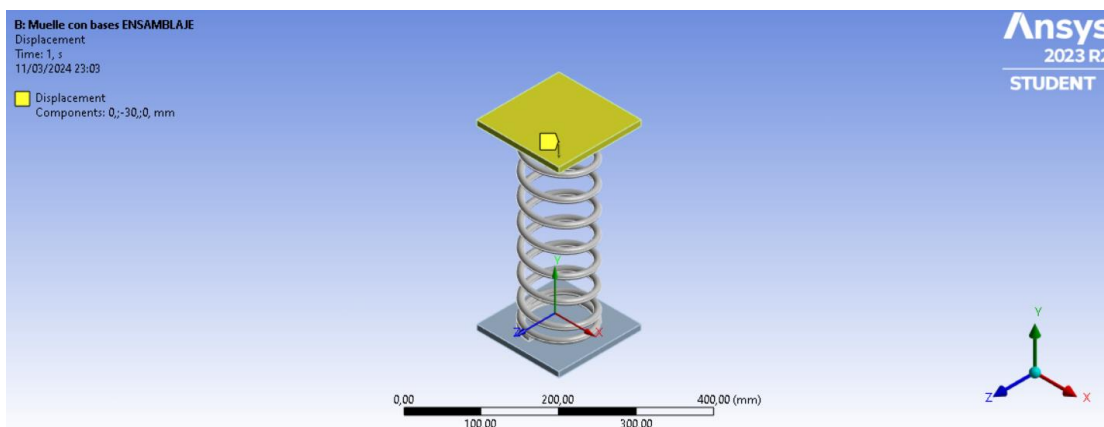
Desplazamiento aplicado en la dirección vertical (eje Y) de la placa superior del muelle.
